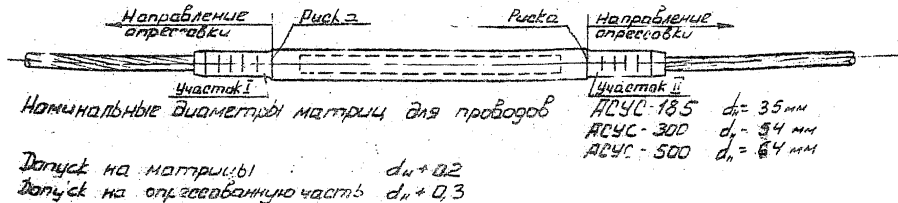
Опрессовка корпуса соединительного зажима САСУС
